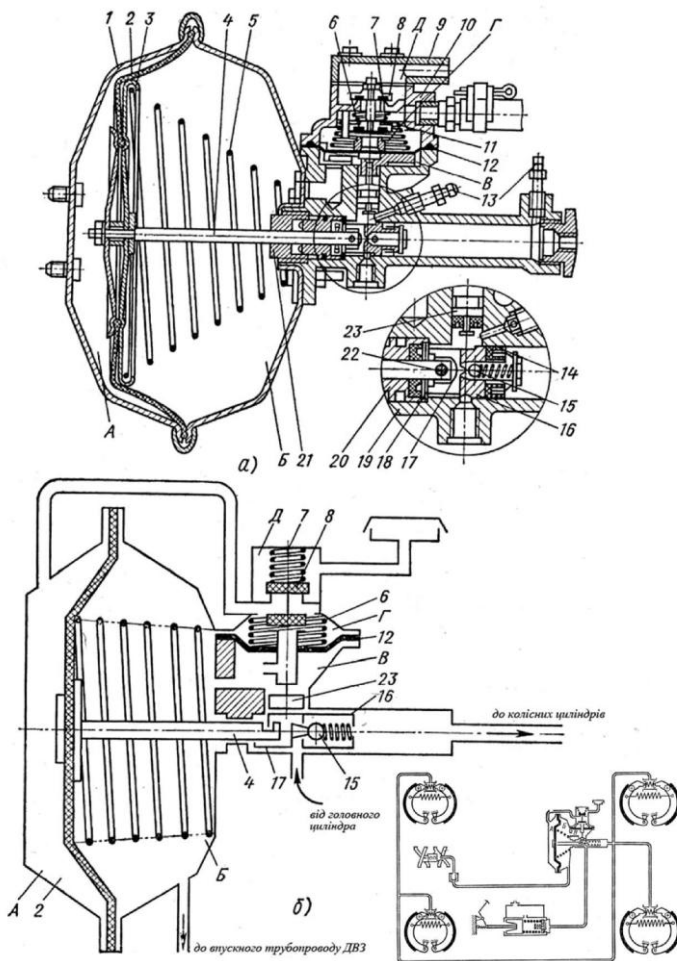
Гідровакуумний підсилювач: конструкція (а) і схема (б) (ГАЗ-53А): 1 - вакуумна камера; 2,12 - діафрагма; 3 - тарілка; 4,17 - штовхач; 5 - конічна пружина; 6 - вакуумний клапан; 7,11 - пружина; 8 - атмосферний клапан; 9 - канал; 10 - корпус слідкувального механізму; 13 - перепускні клапани; 14 - манжета; 15 - кульковий клапан; 16 - поршень; 18 - упорна шайба; 19 - циліндр; 20 - ущільнювальний корпус; 21 - гайка; 22 - штифт; 23 - плунжер; А-Д- порожнини.
